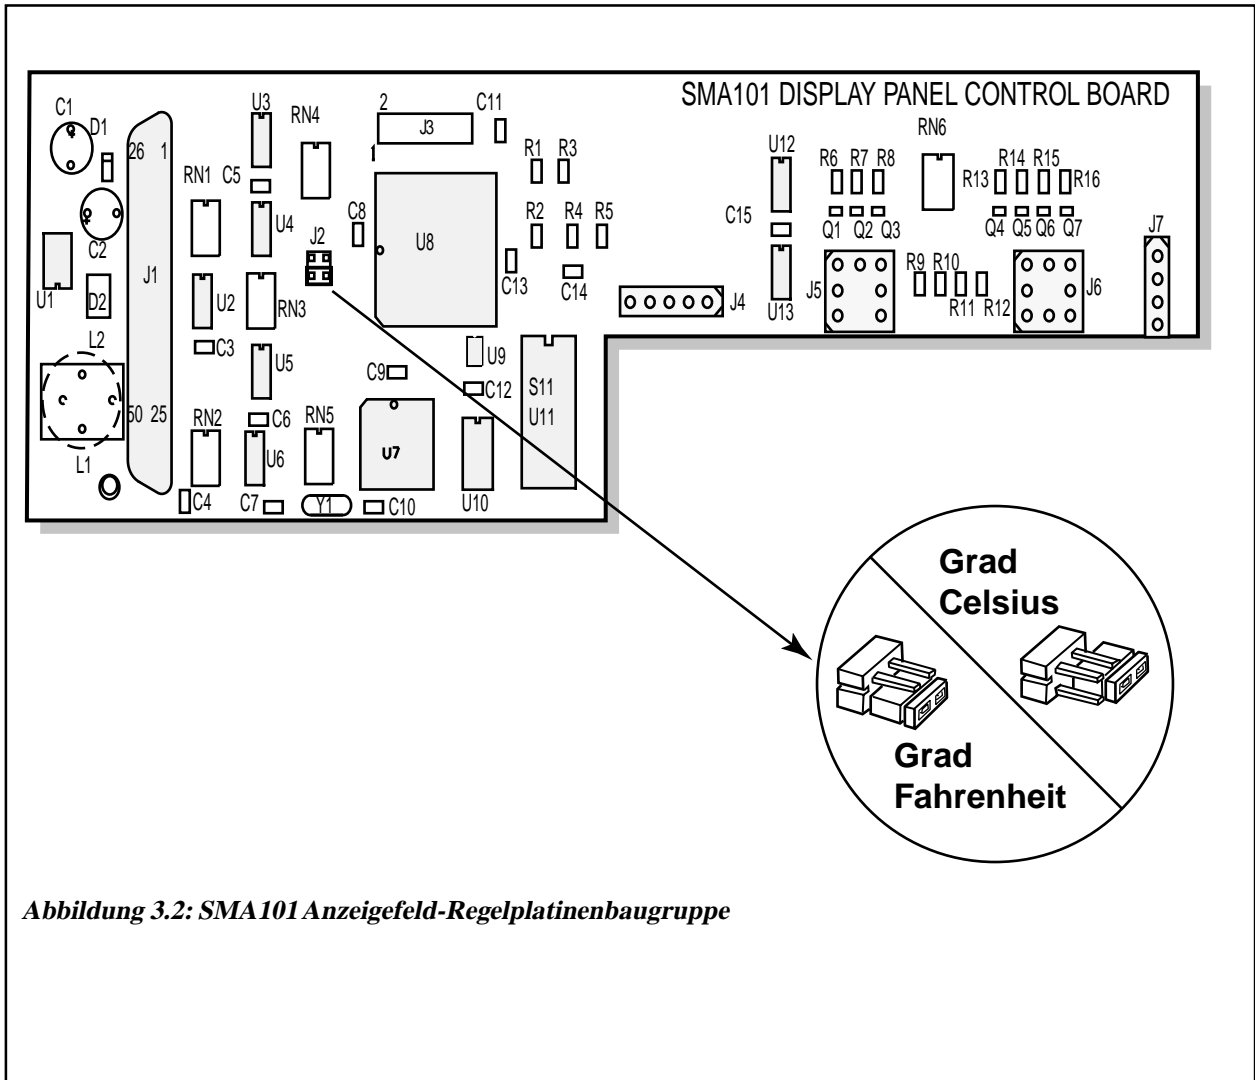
SMA101 Anzeigefeld-Regelplattenbaugruppe
